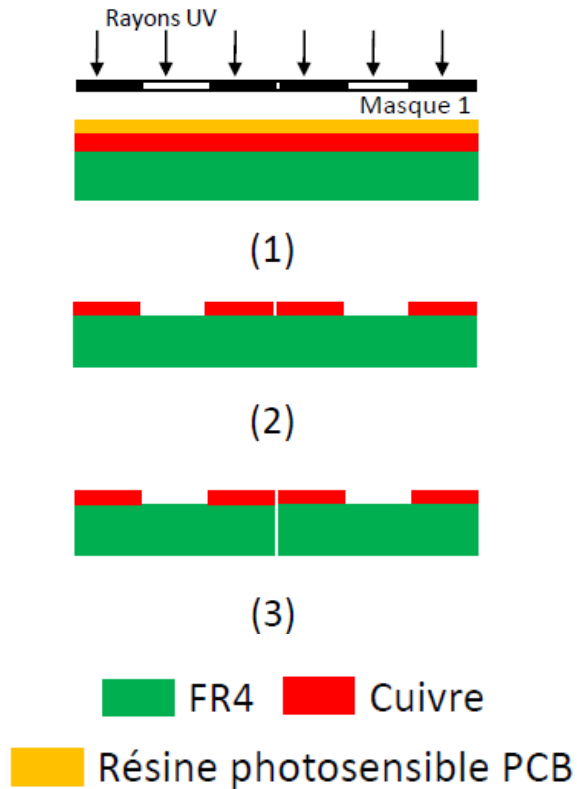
Processus de fabrication de la plaque inférieure PCB
